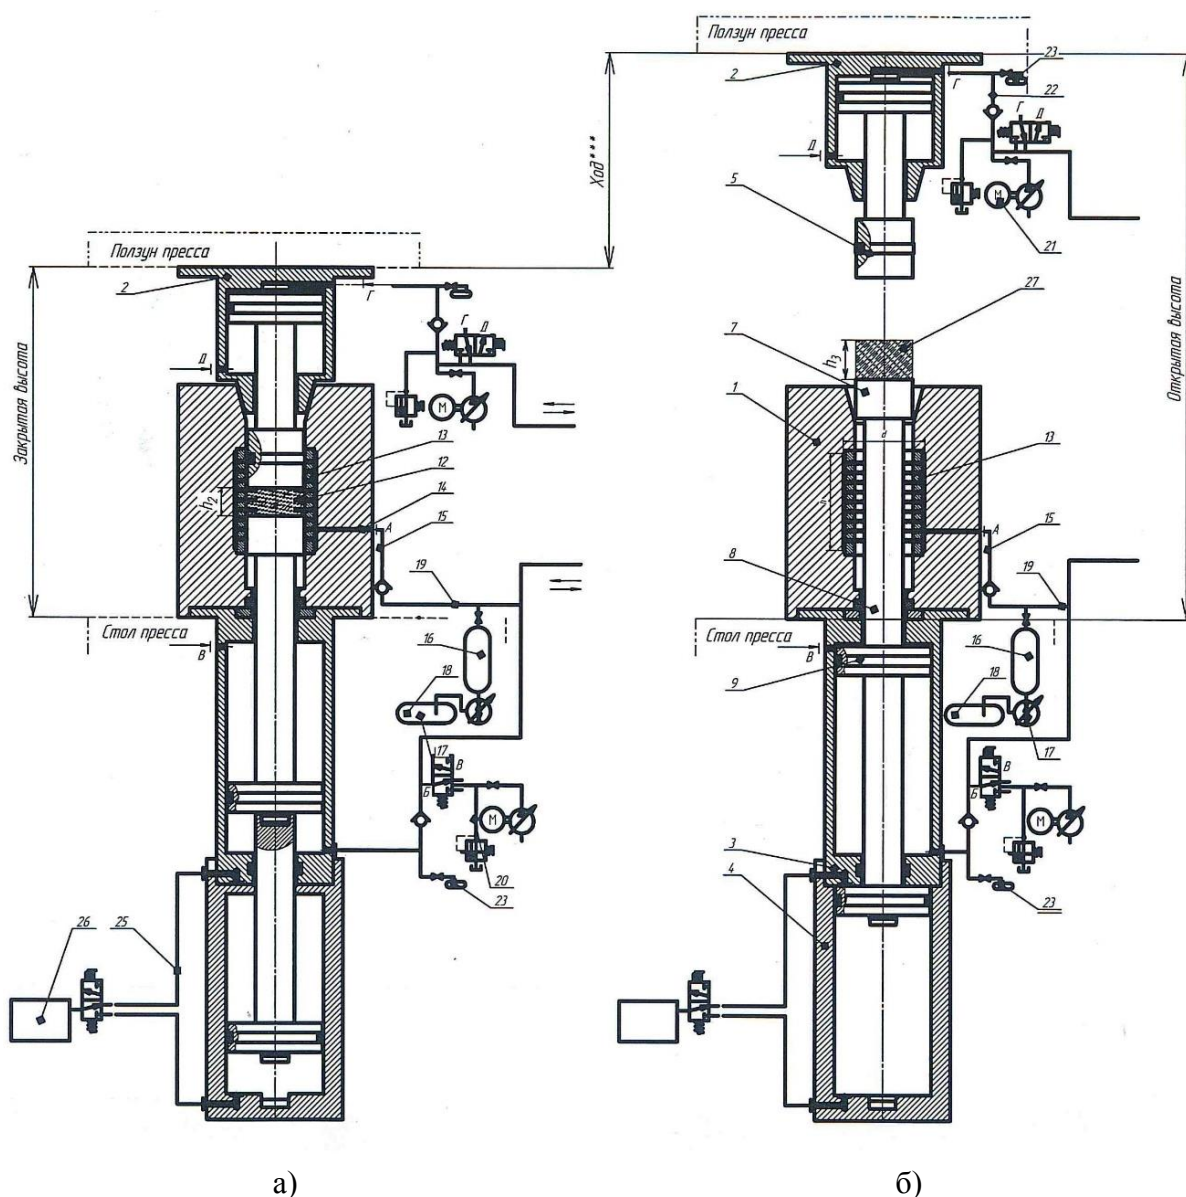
Схема работы устройства СВС-баротермии – допрессовка и удаление синтетической заготовки
